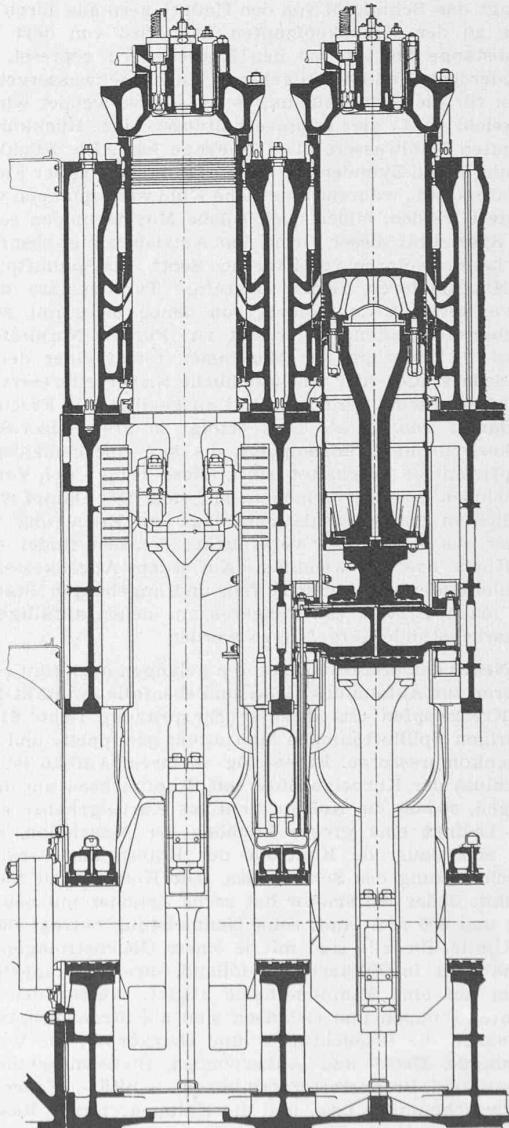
Längsschnitt durch zwei Zylinder einer Hauptmaschine
